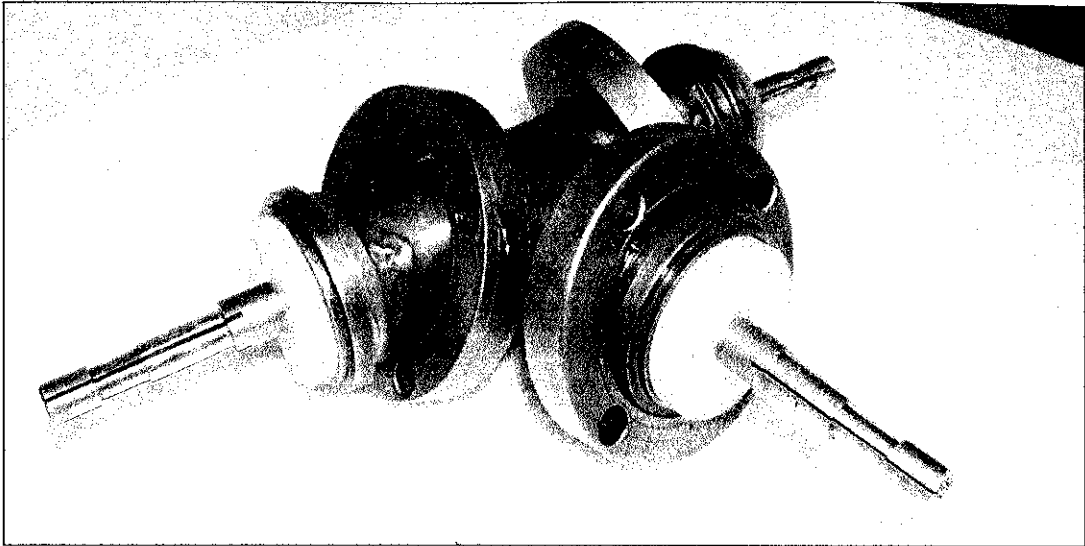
ข ภาพวาดแสดงการออกแบบ Swivel Flange (Ring)
